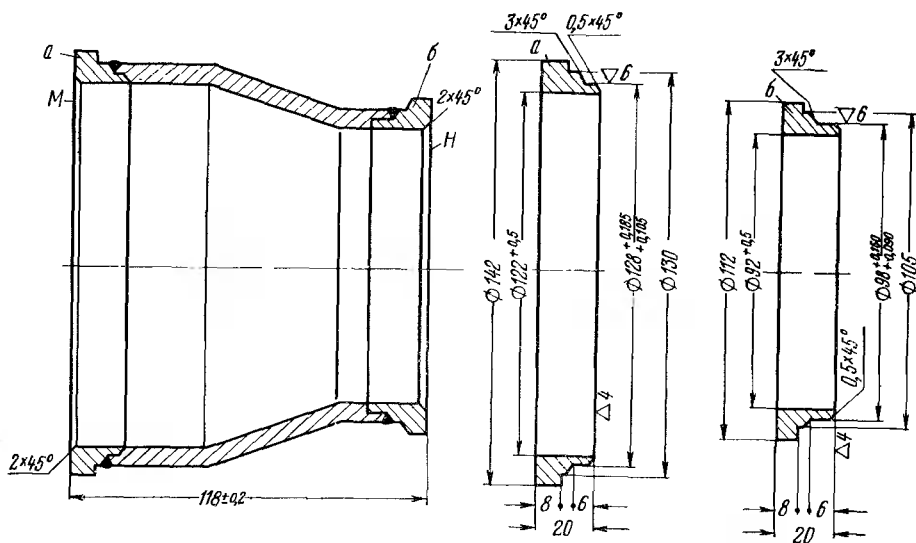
Ремонтные втулки распорного кольца подшипников ступицы заднего колеса:
